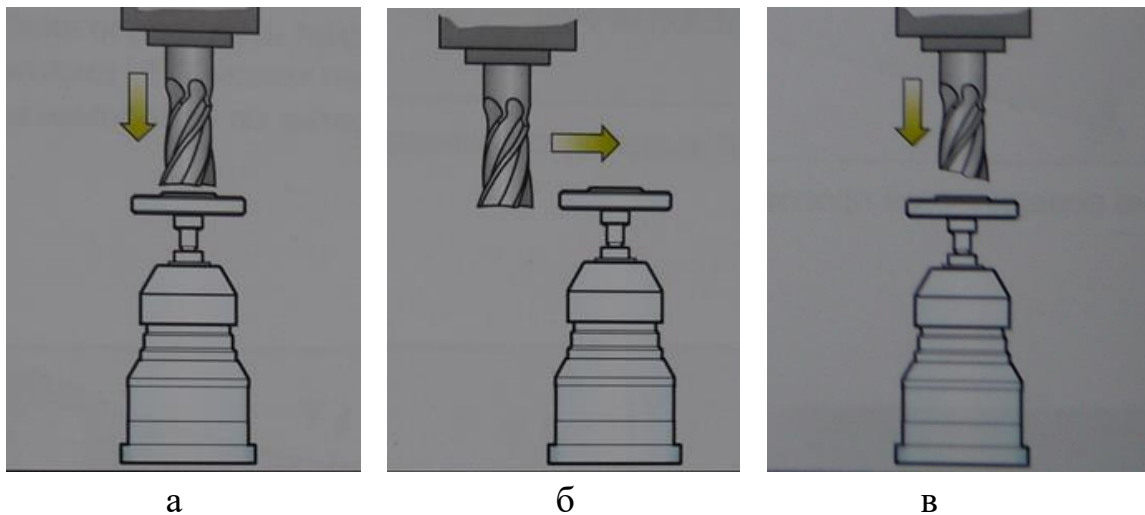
Принципова схема вимірювання інструменту на верстаті: а- вимірювання довжини; б- вимірювання діаметру; в- контроль поломки
